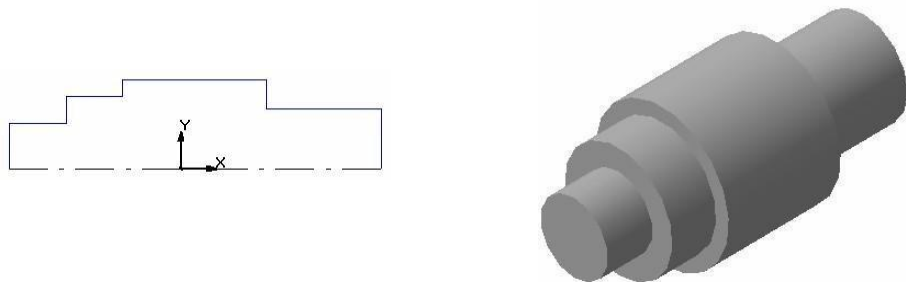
Ескіз і деталь типу “Вал”, утворена операцією обертання кінематична – створення об’ємного елемента (деталі) шляхом переміщення ескізу вздовж зазначеної напрямної (рисунок. 3.4);
